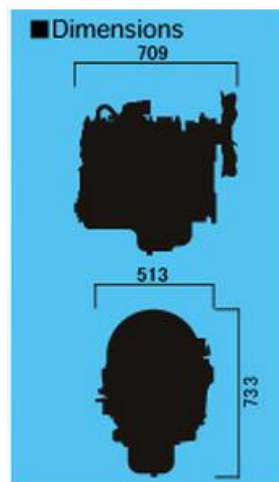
Dimensiones TOYOTA 4Y [3]
